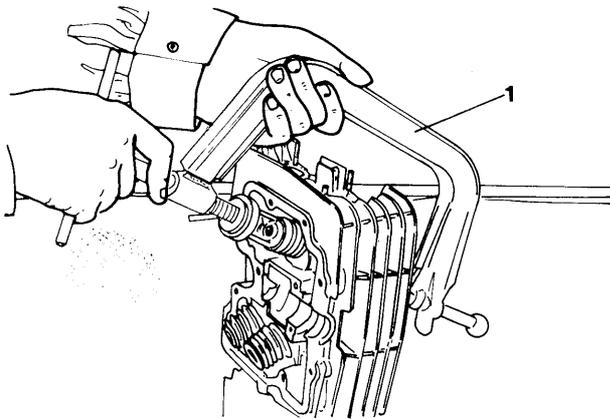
Ventile mit einer Ventilefederzange (1) entfernen.
